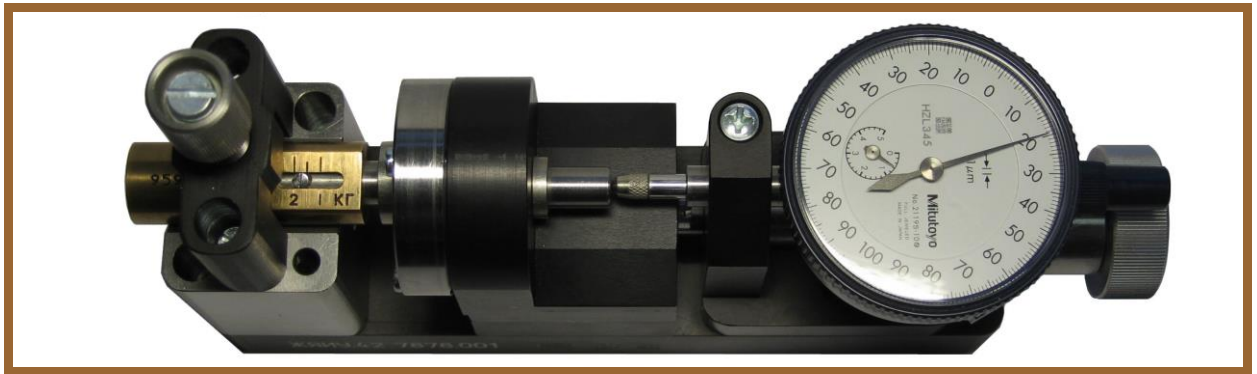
А – УПД с установленным приспособлением 959 49 66.
